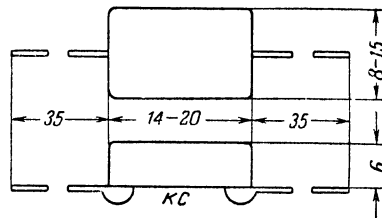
Габаритный чертеж стеклоэмалевых конденсаторов.
